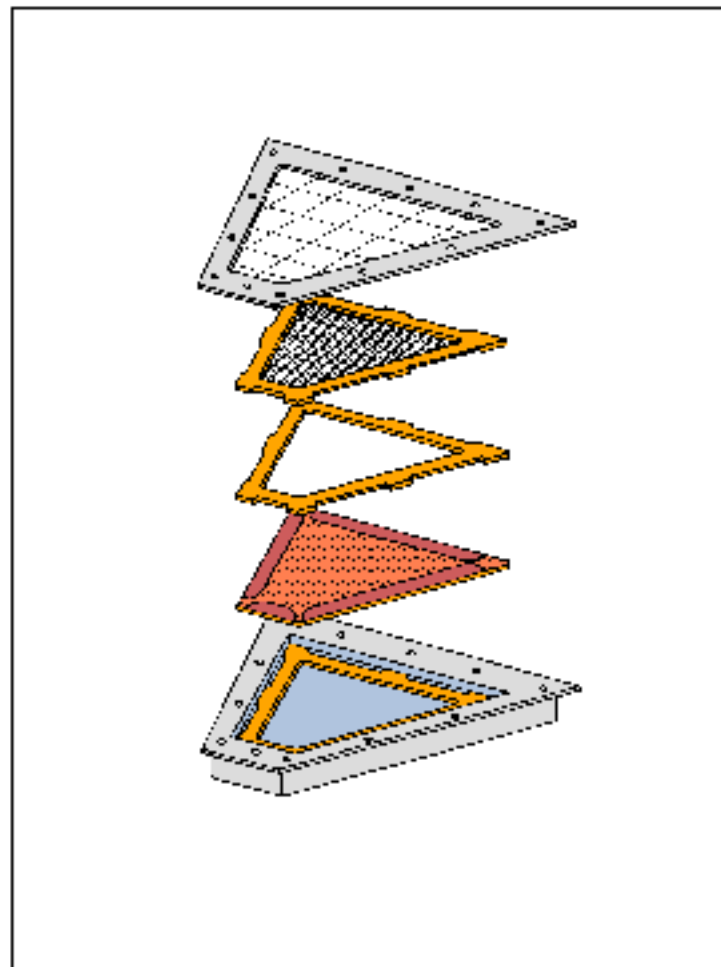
Explosionszeichnung eines Parallelplattenzählers.
